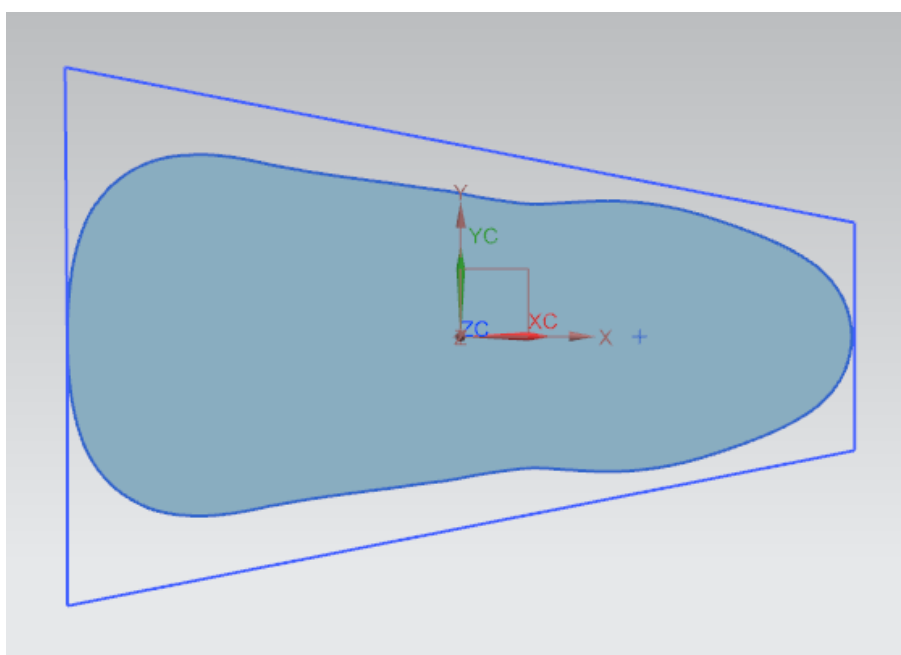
Заготовка, полученная разверткой, вписанная в размеры заготовки, заданной существующей технологией
